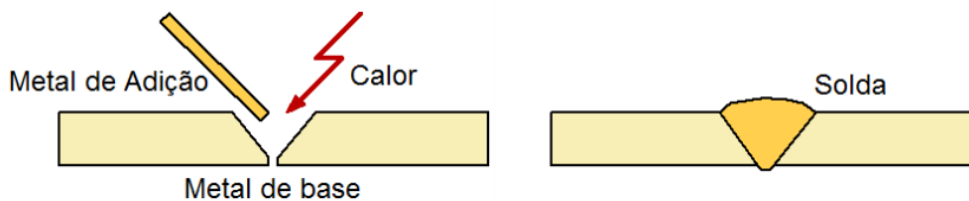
Ilustração da soldadura por fusão [53]
